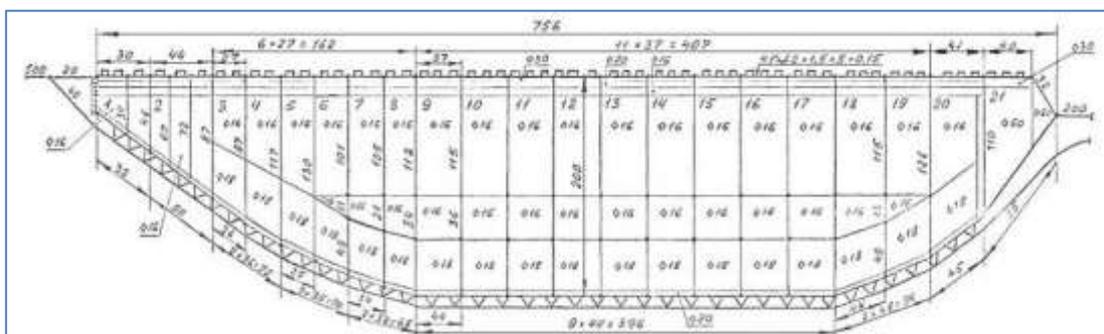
Сборочный чертёж невода кошелькового 756x220 м
